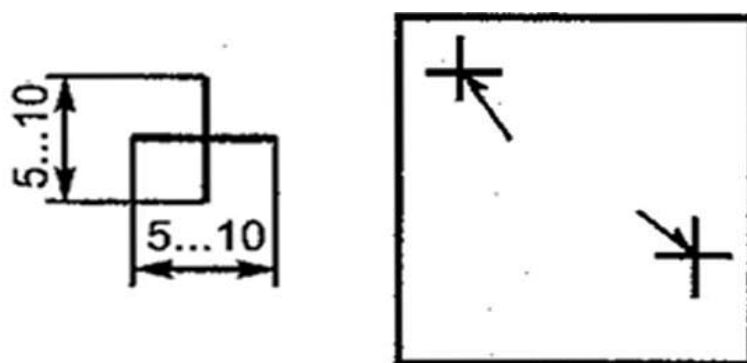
Обозначение видимой одиночной сварной точки
